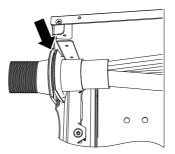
Вставка кабеля и втулки в паз корпуса
